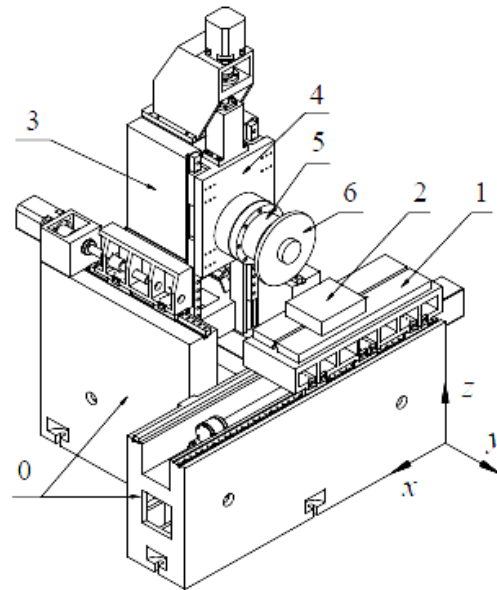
Триосьовий плоскошліфувальний верстат з ЧПК (0-передня-задня станина верстата, 1-робочий стіл, 2-заготовка, 3-колона, 4-шпиндельна коробка, 5-шпиндель, 6-шліфувальний круг)
